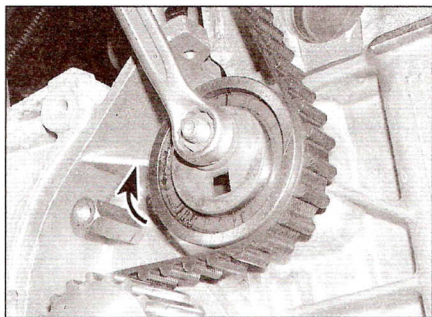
Отверните гайку и поверните натяжной шкив по часовой стрелке, чтобы снять натяжение с ремня газораспределительного механизма (двигатели 1.4 л)
